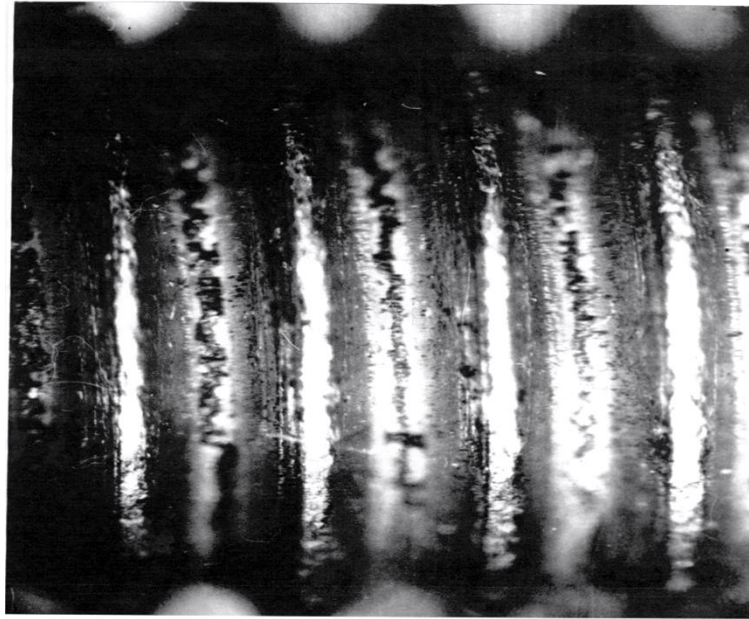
Резьбовой образец с усталостными трещинами во впадинах резьбы
